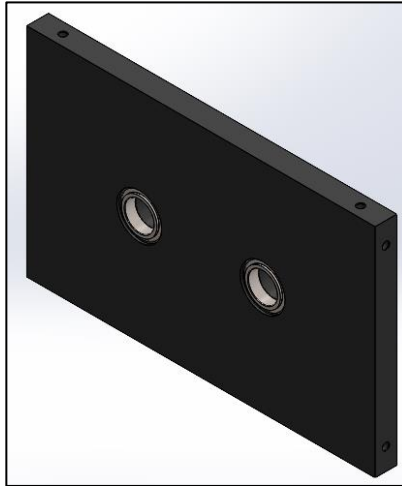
Vista isométrica de la pared frontal de la cámara de trituración con rodamientos en SolidWorks
